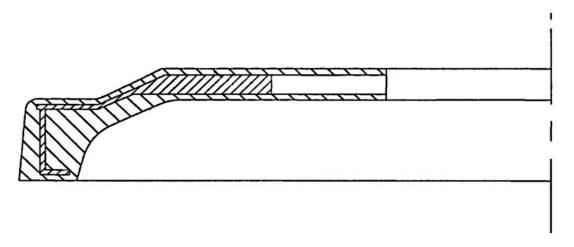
Пример изготовления тонкостенной детали – основание (повторение контура чистовой детали)
